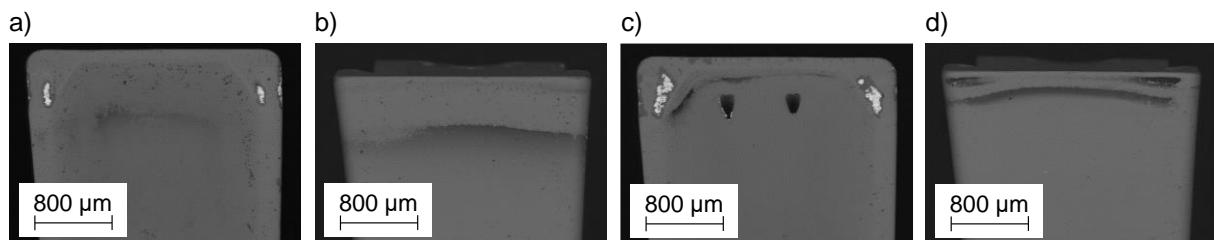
Werkzeugschneiden nach Erreichen des Abbruchkriteriums bei der Bearbeitung von X5CrNi18-10; a) Spanfläche des Referenzwerkzeuges, b) Freifläche des Referenzwerkzeuges; c) Spanfläche des microCutOff-Werkzeuges, d) Freifläche des Referenzwerkzeuges
